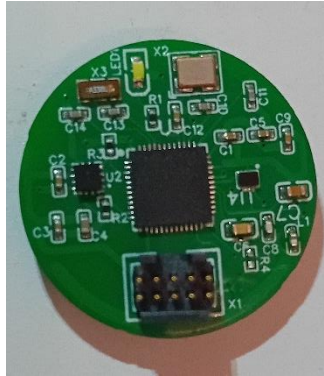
Parte superior BLE\_PCB\_V2 sin ensamblar
